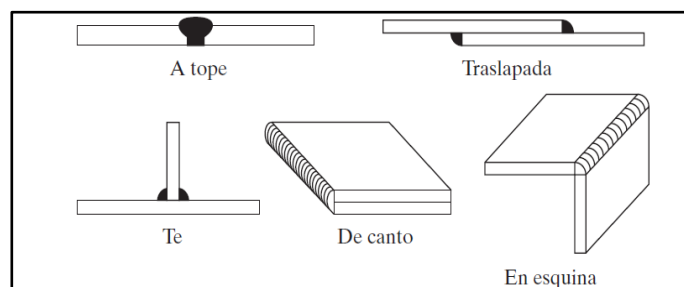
Tipos de juntas en soldadura. McCormac, *Diseño de Estructuras de Acero 5ta. Edición* (2012)
